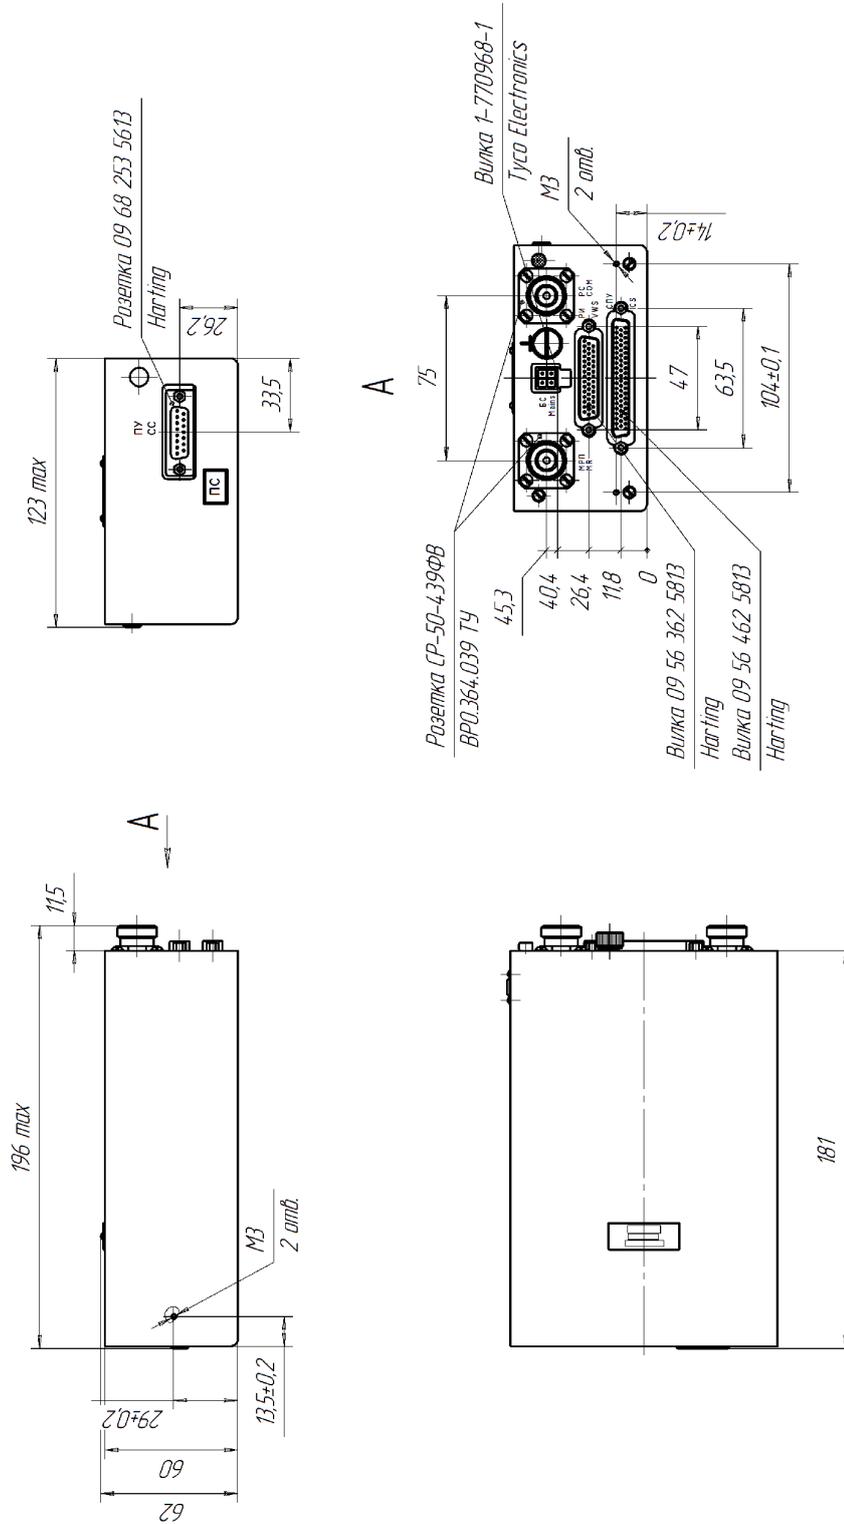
Габаритный чертеж блока Б1-ПрМ
